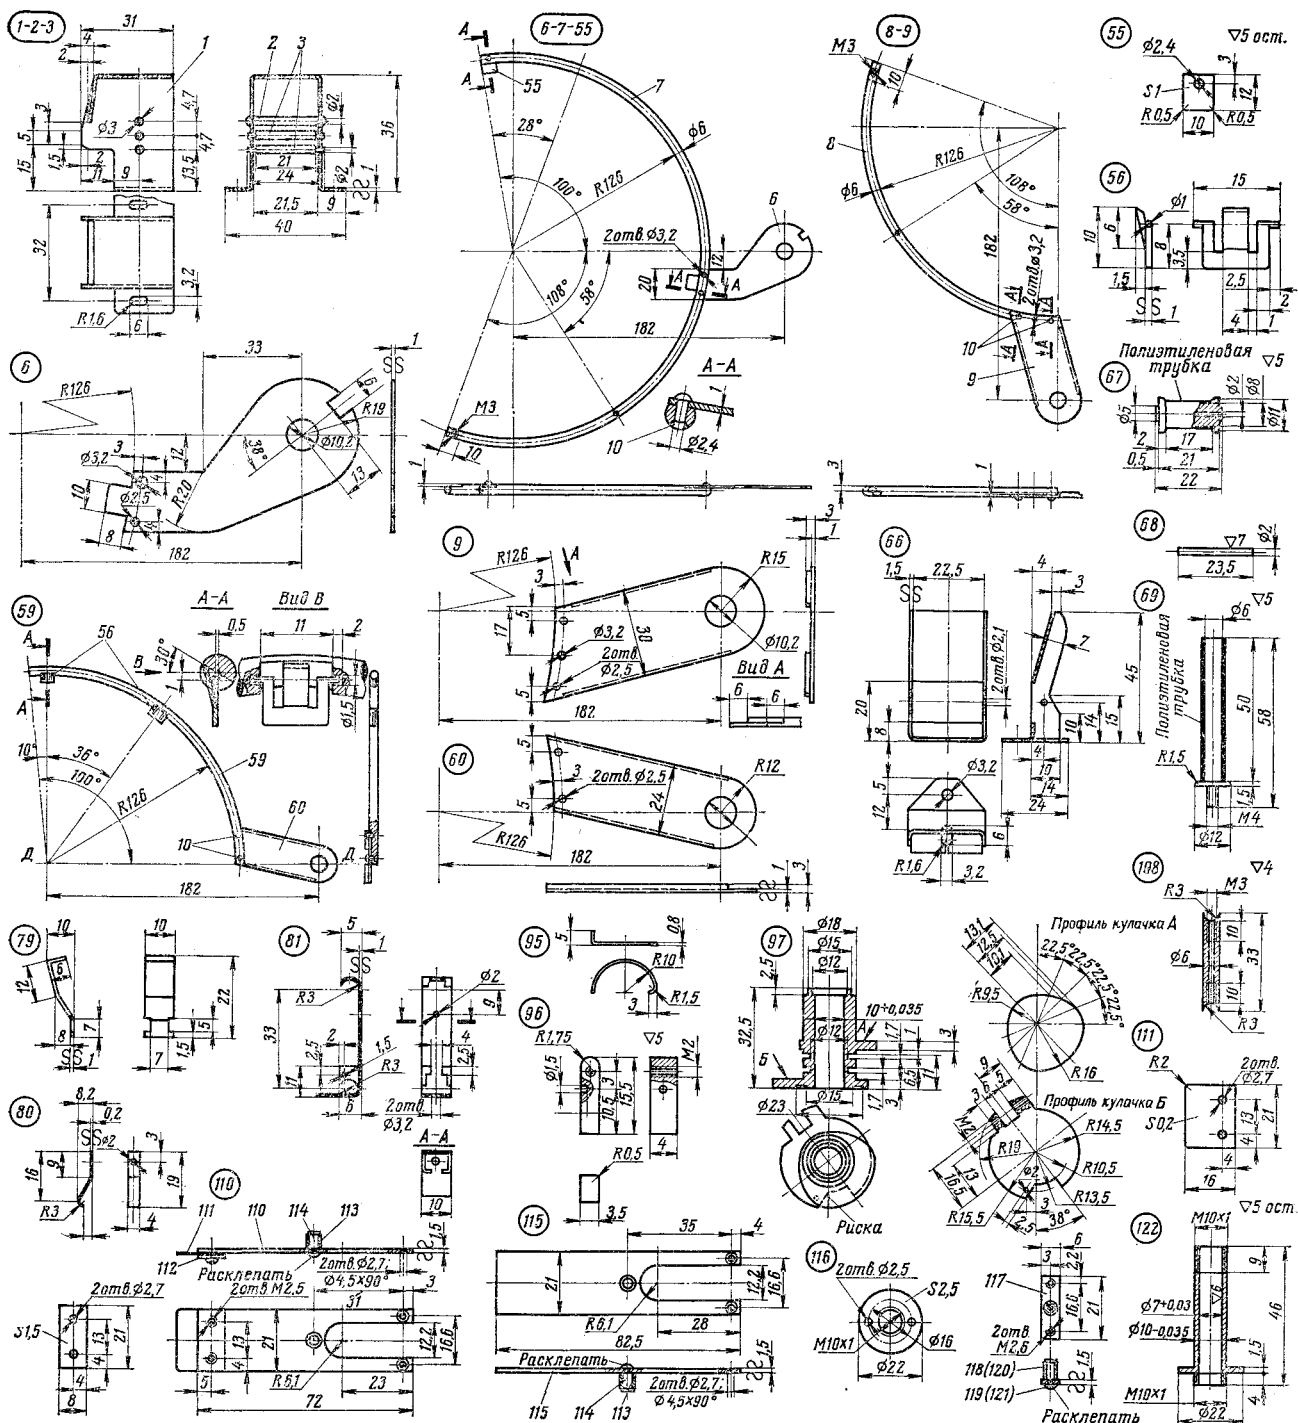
Детали механизма смены пластинок: 1 — кронштейн, Ст.10кп; 2 — валик, Ст.45, расклепать при сборке в детали 1; 3 — валики, Ст.45, 2 шт.; 4 — пластина нижнего ухвата, Ст.10 кп; 5 — нижний ухват, Ст.45, закрепить на детали 6 заклепкой 10; 6 — верхний ухват, Ст.45, закрепить на детали 7 двумя заклепками 10; 7 — пластина верхнего ухвата, Ст.10 кп; 8 — заклепки стальные 2,4×8, 6 шт.; 9 — держатель нижний, Ст.10 кп, закрепить на детали 7 заклепкой 10; 10 — держатель верхний, Ст.10кп, 2 шт.; 11 — поворотная часть верхнего ухвата, Ст.45,
